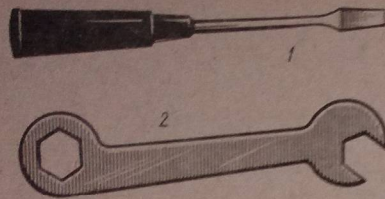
Инструмент: 1 — отвертка; 2 — гаечный ключ
